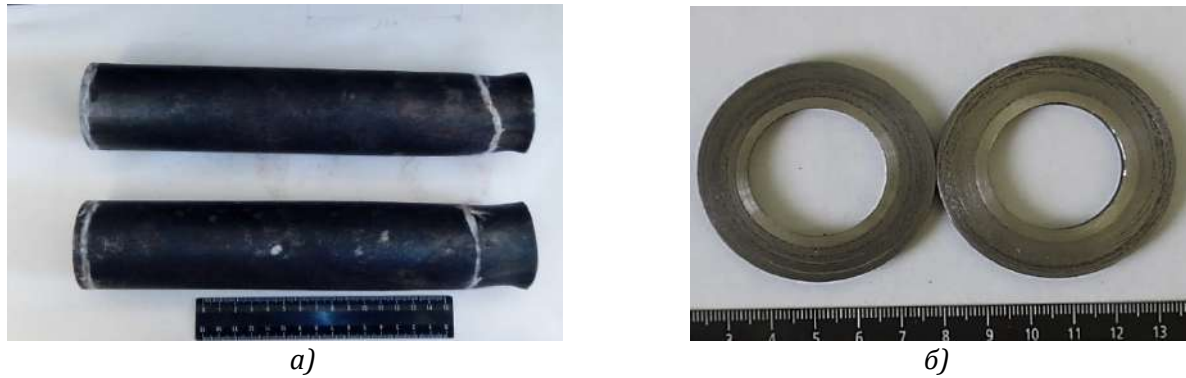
Биметаллические трубные заготовки: а – после ультразвукового контроля; б – кольцевые биметаллические образцы (внутренний слой – жаропрочный сплав, наружный – сталь ОХНЗМ)
